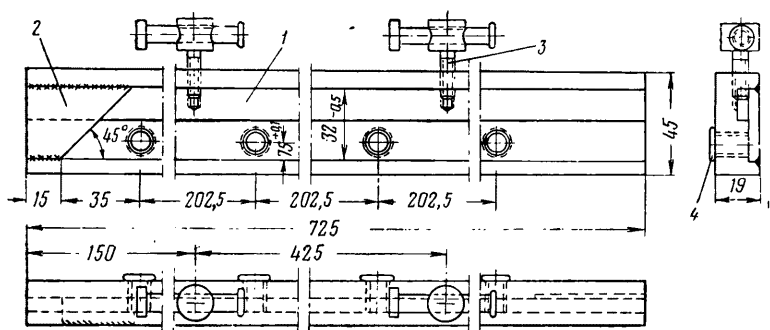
Кондуктор для сверления отверстий в накладках полоза:
